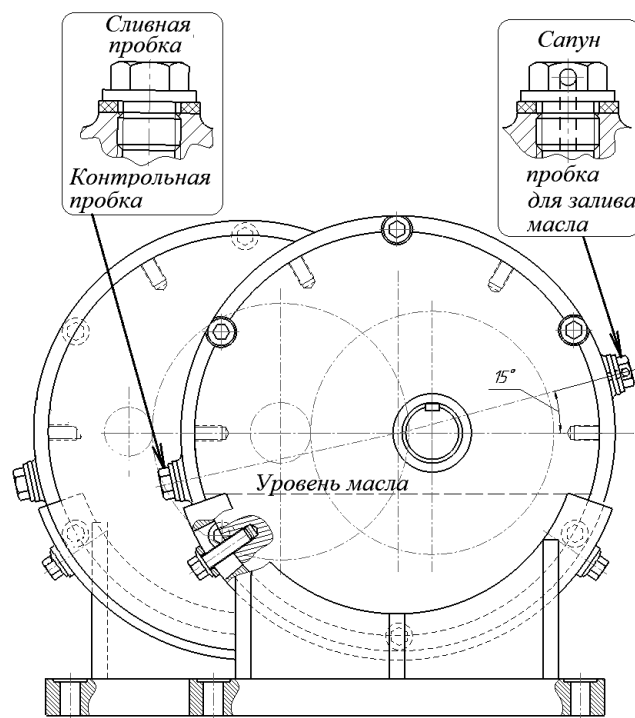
Устройства вентиляции и контроля уровня масла в редукторе
